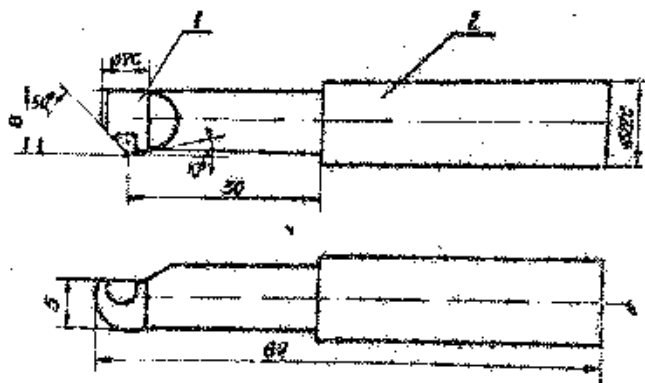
Сварной резец: 1 – вставка с режущим элементом из ПСТМ на основе нитрида бора типа ИС 005.00.01; 2 – державка
